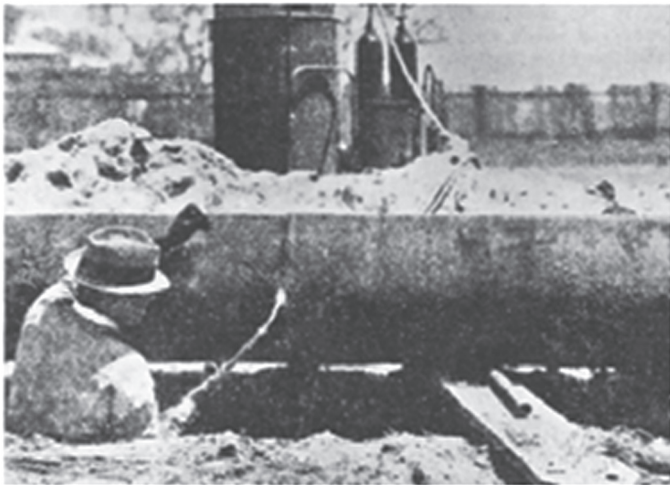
Montagem de tubulações de aço pelo processo de soldagem oxiacetileno no início de 1920 [68].
